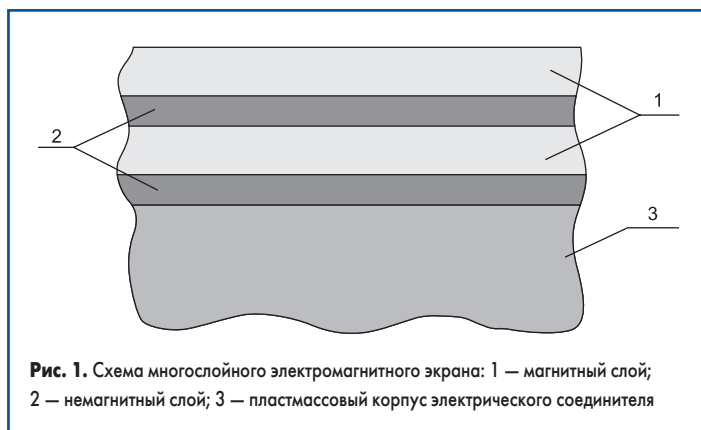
Схема многослойного электромагнитного экрана: 1 — магнитный слой; 2 — немагнитный слой; 3 — пластмассовый корпус электрического соединителя
